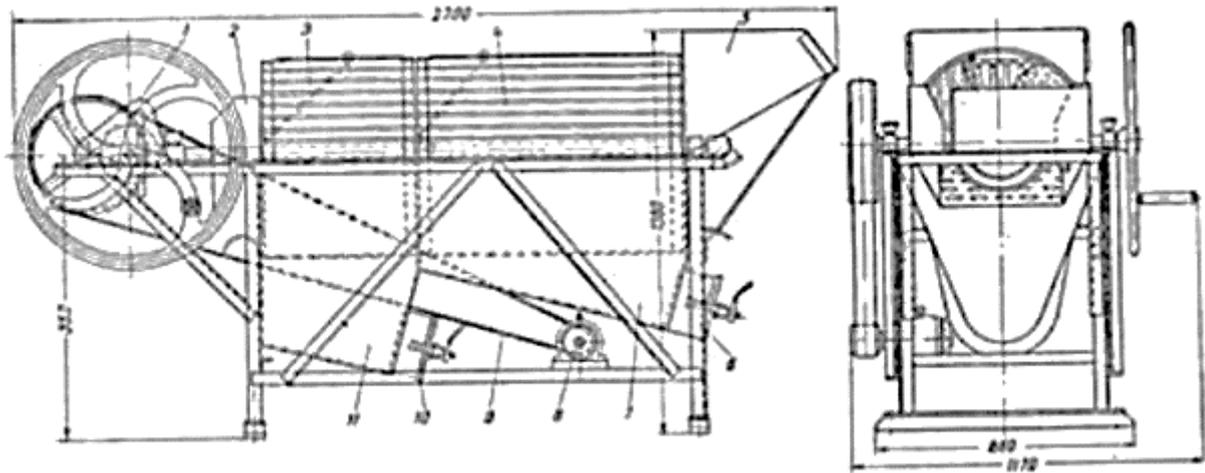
Схема двокамерної барабанної коренебульбомийки: 1 – кожух передавального механізму; 2 – випускний лоток; 3, 4 – мийні барабани; 5 – завантажувальний лоток; 6, 10 – грязьові люки; 7, 11 – корита для води; 8 – електродвигун; 9 – приводний ремінь.
